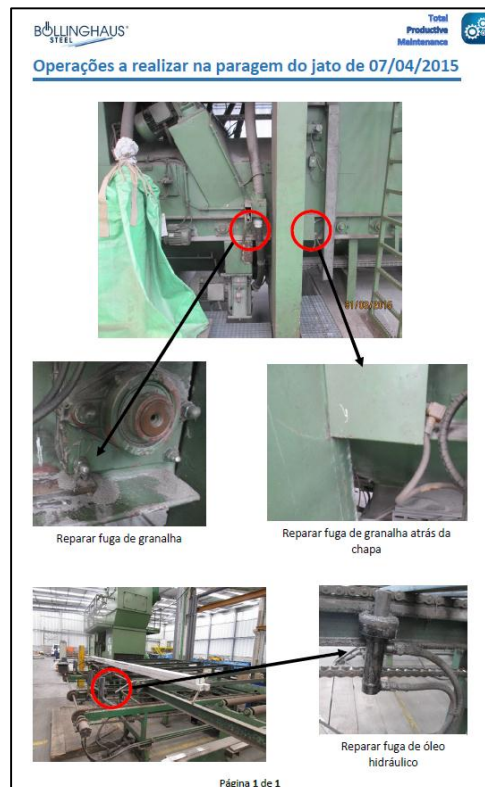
Lista de operações a realizar nas paragens planeadas
